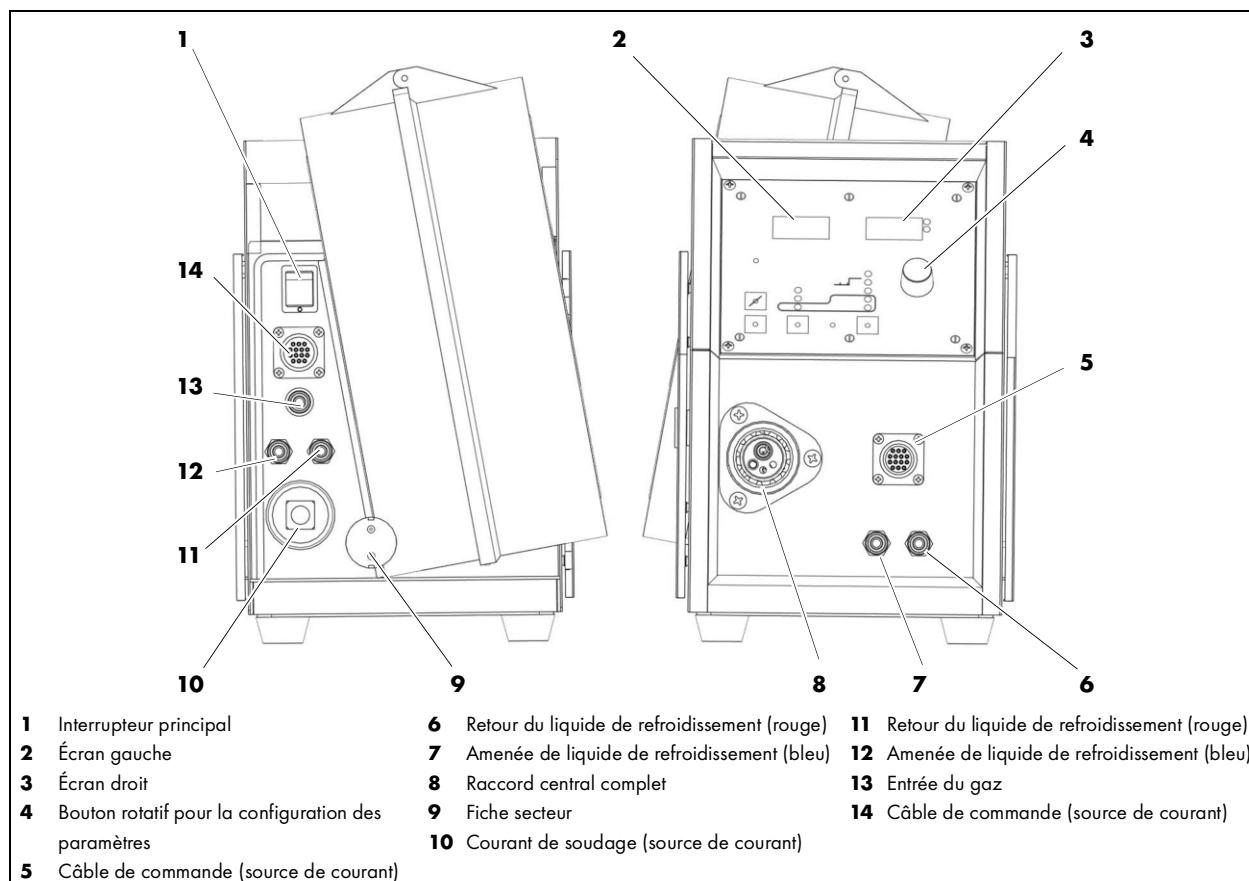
Vue d'ensemble des raccords et éléments de commande
